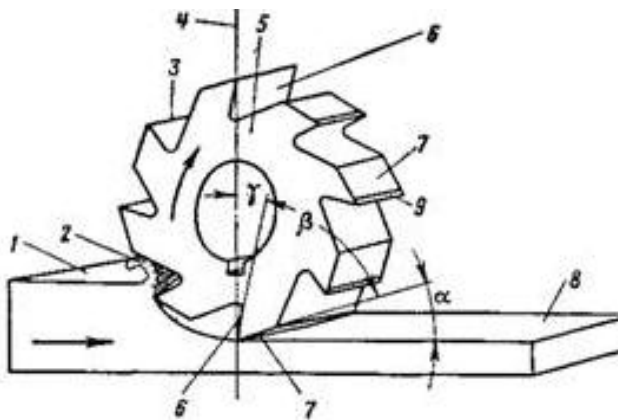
Геометричні параметри циліндричної фрези: 1 – заготовка; 2 – стружка; 3 – різальна кромка; 4 – вісь фрези; 5 – корпус; 6 – передня поверхня; 7 – задня поверхня; 8 – оброблена поверхня заготовки; 9 – стрічка; кути фрези: γ – передній, α – задній, β – кут нахилу зубця фрези
